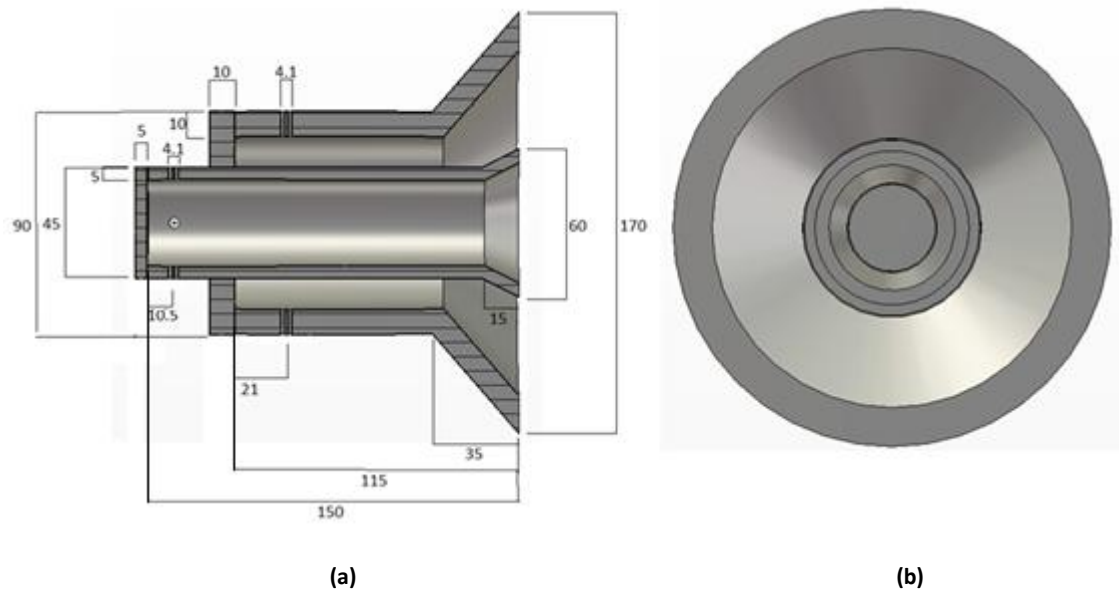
Planos en mm del diseño final de la antena para su fabricación. Corte perfil (a) y alzado (b).
